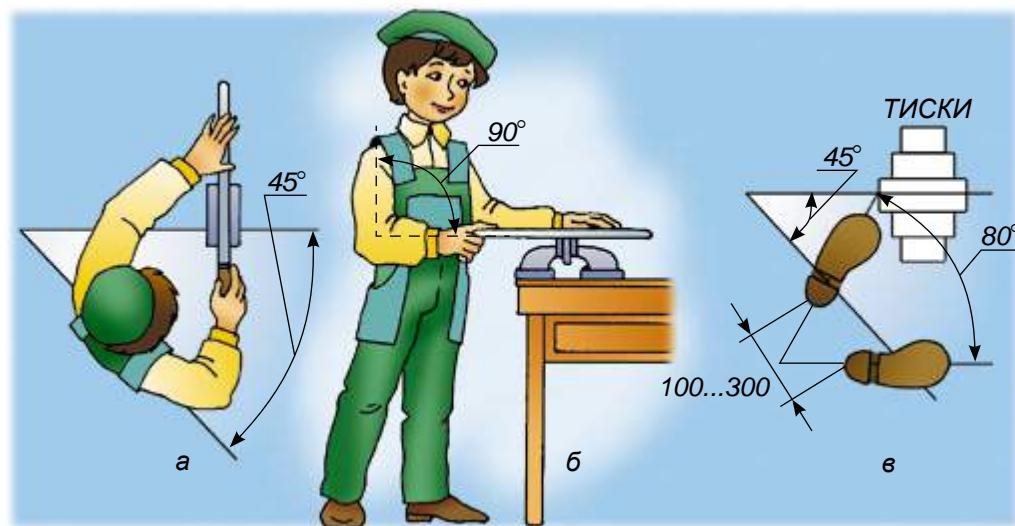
Положение при опиливании: а – туловища; б – корпуса тела человека; в – ступней ног
